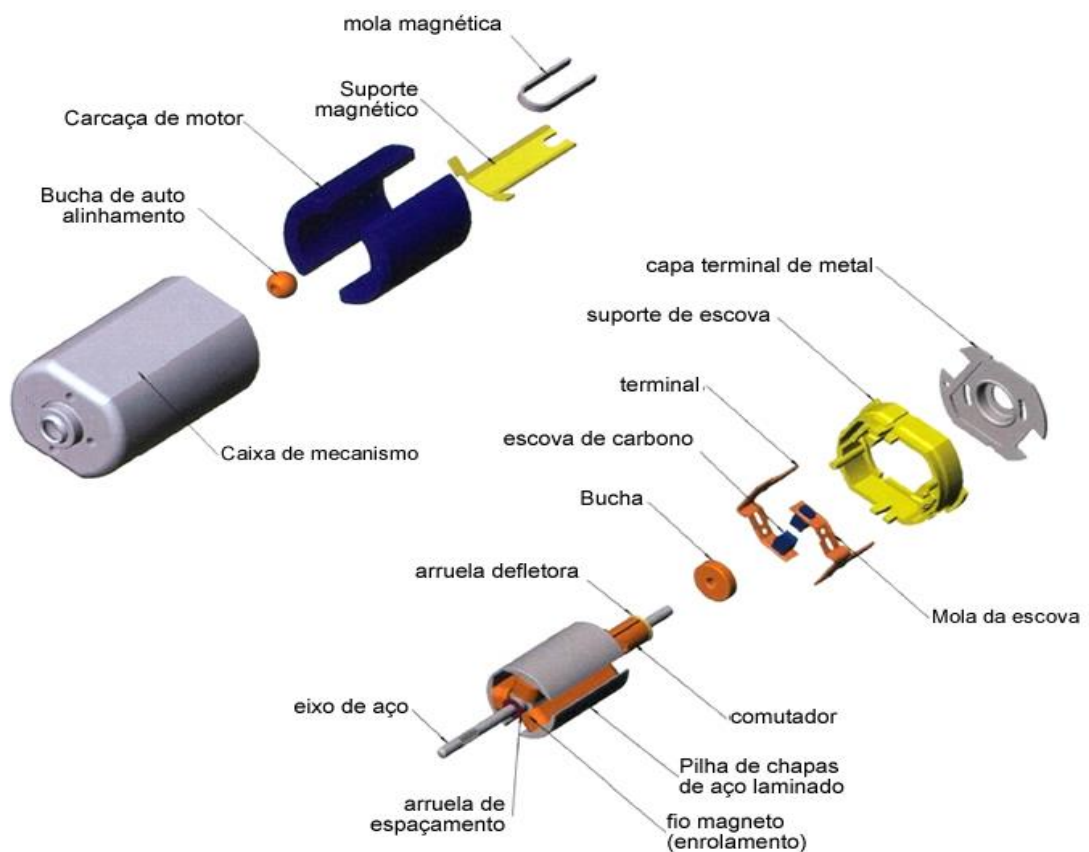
Vista Explodida do Motor DC. Extraído de [26]
